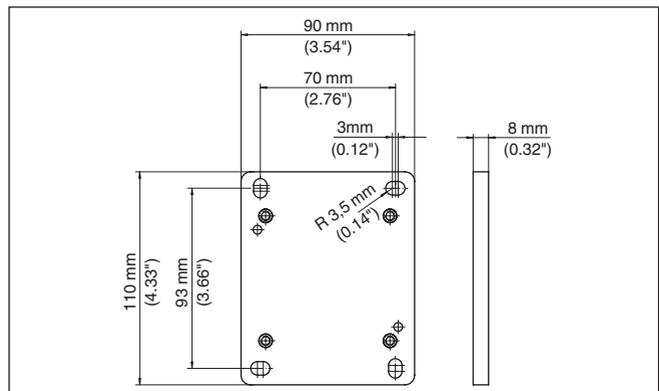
Bohrbild - Wandmontageplatte (externes Gehäuse)
